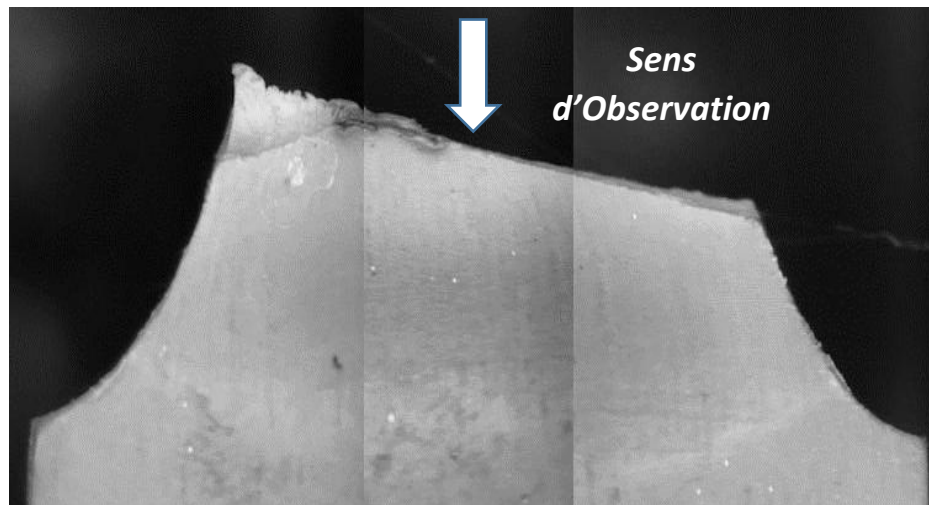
Photographie macroscopique d'une éprouvette après rupture
